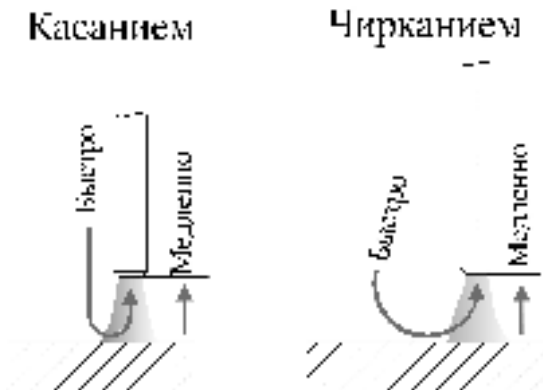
Способы зажигания сварочной дуги.
